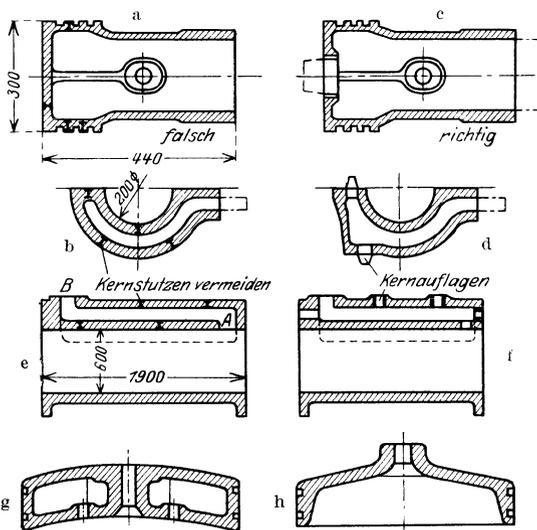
bis h. Maschinenteile ohne und mit Kernauflagen.
